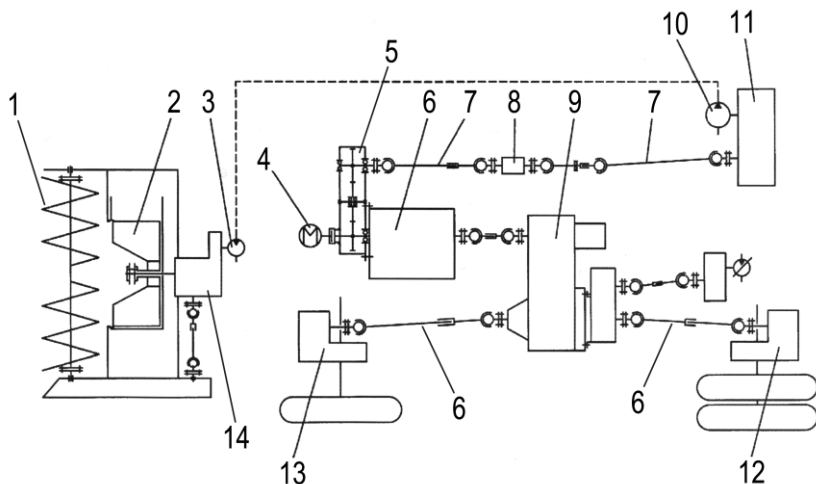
Кинематическая схема гидромеханического привода рабочего органа фрезерно-роторного снегоочистителя:
